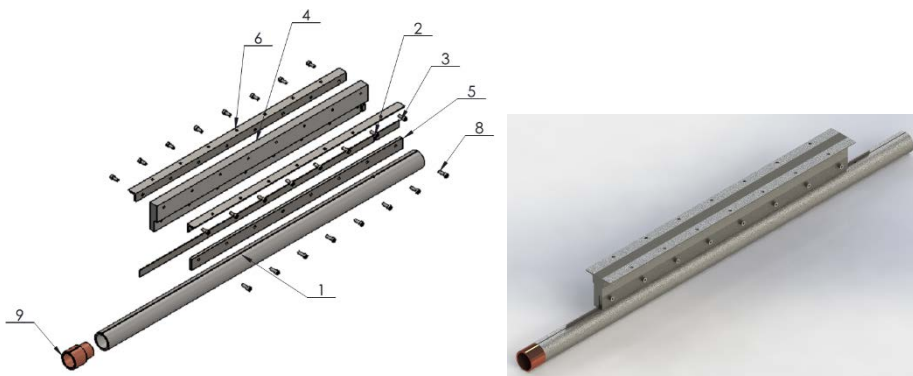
Mecanismo suporte da conduta, representado em vista isométrica explodida e montada
